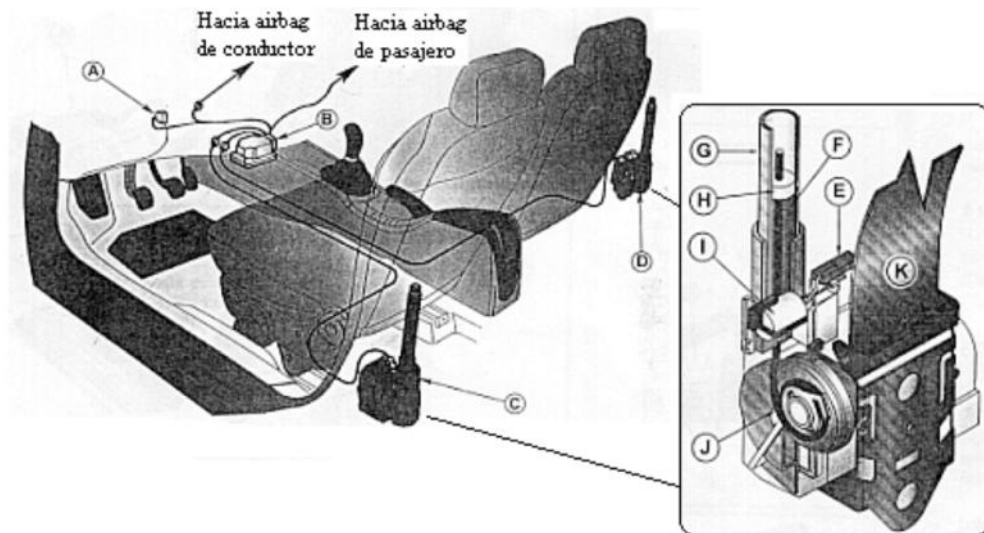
Pretensores por bobinador pirotécnico y mando electrónico
